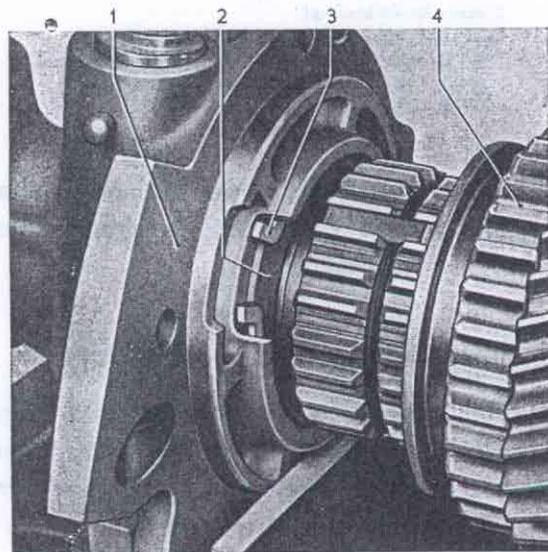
Sprengring für Kugellager in Getriebegehäuseverlängerung eingebaut
